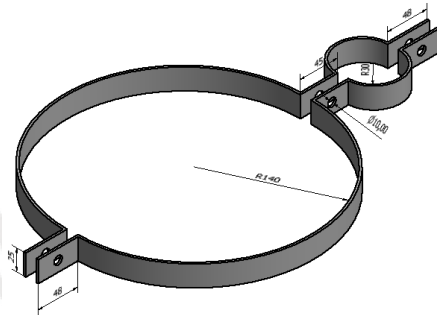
Dimensiones de abrazadera del soporte tubular
